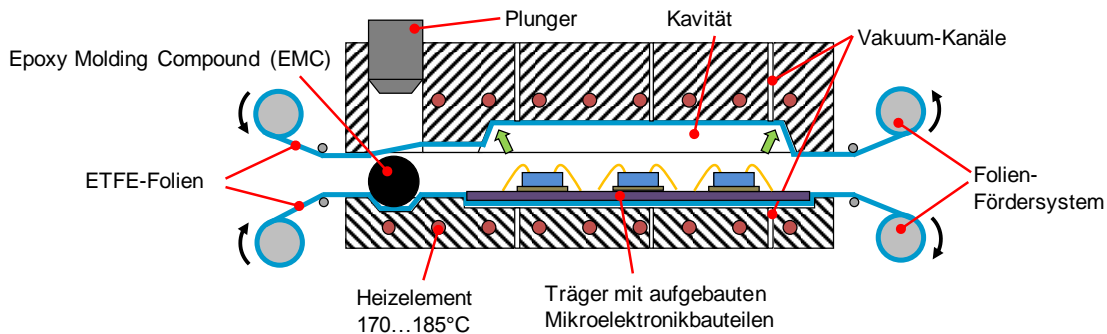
Prinzipskizze des Film-Assisted Transfer Moldings.
